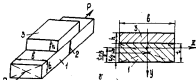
В примере 2.2.1: а - схема составного стержня; б - поперечное сечение по стыку; в - сечение вала; 2 - сварной шов; 3 - накладка
